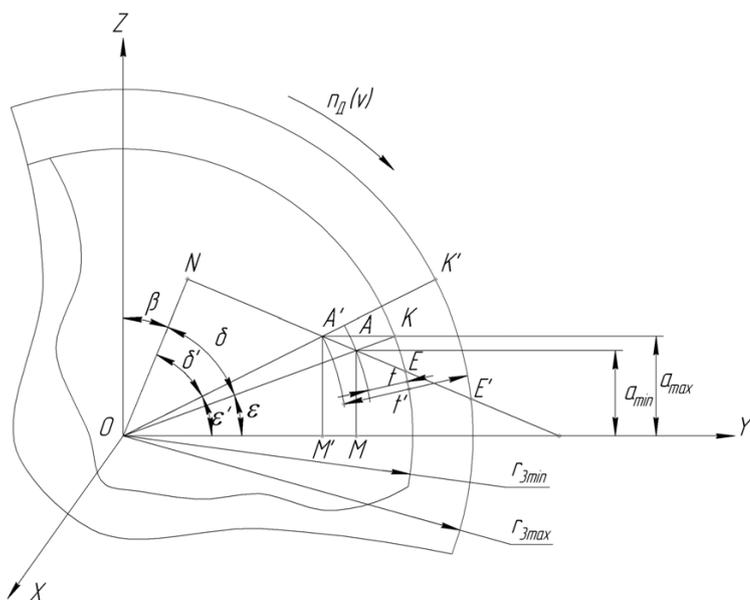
Схема определения угла поворота заготовки до первого касания передней поверхности инструмента с поверхностью резания
